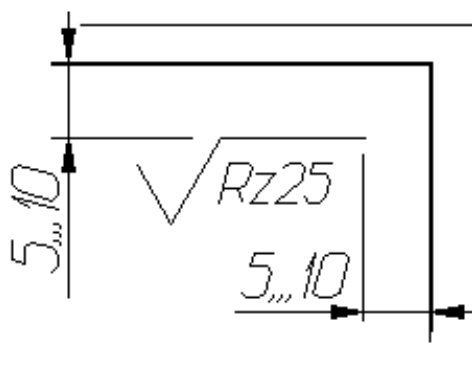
Указание шероховатости одинаковой для всех поверхностей изделия
